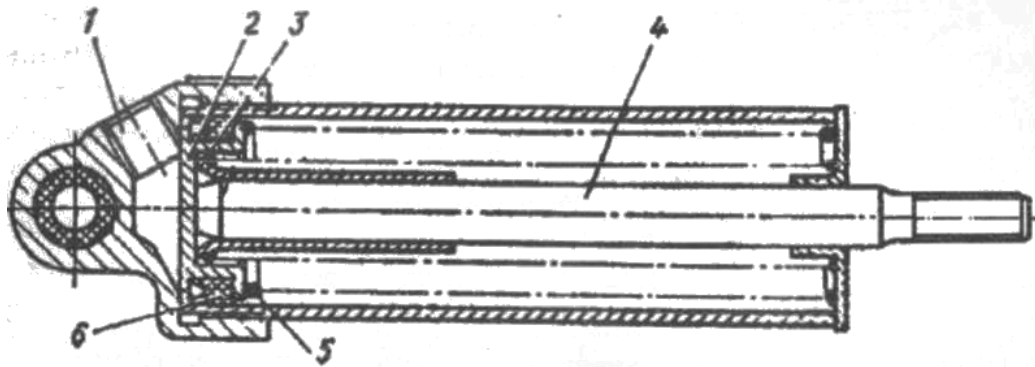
Пневмоцилиндр привода заслонки механизма вспомогательного тормоза:
